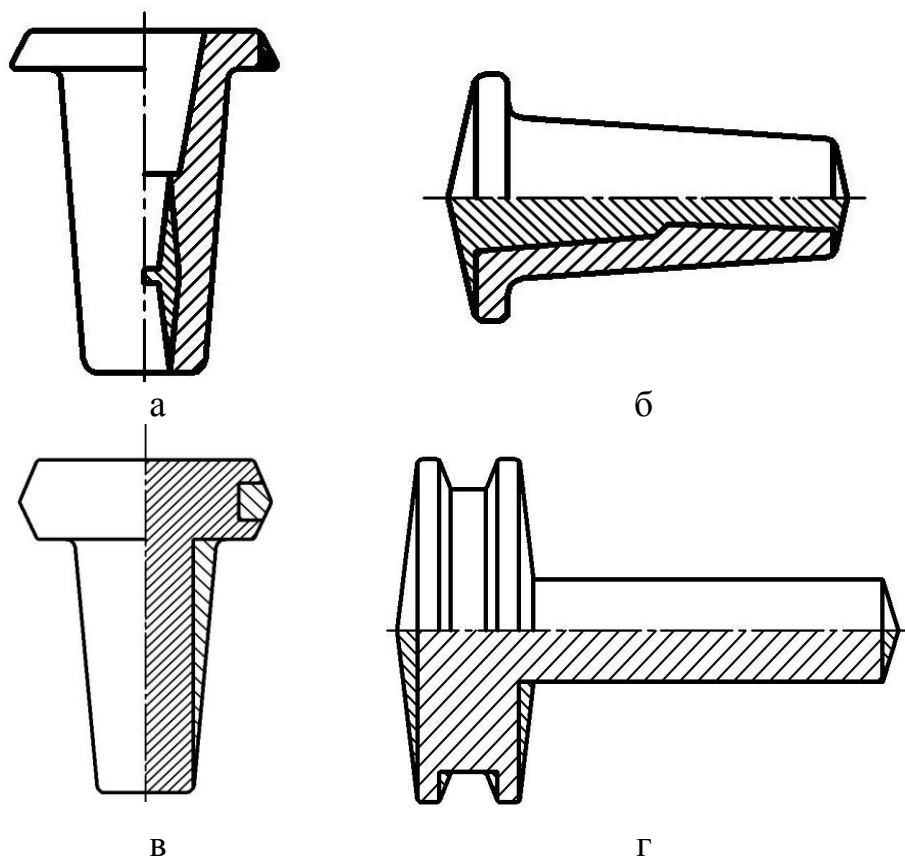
Вплив розташування поверхні розніму штампа на форму поковки
